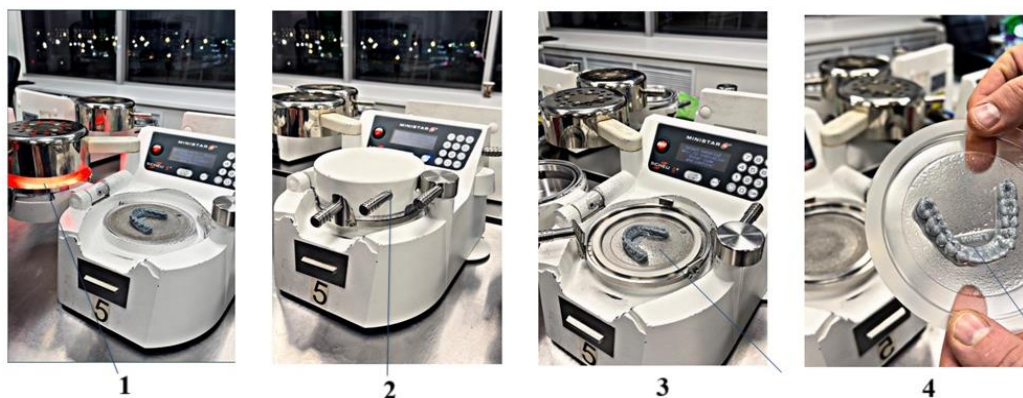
Термоформовочный агрегат фирмы Shueu-Dental, модель Ministar-S для изготовления элайнеров. 1 – ИК излучатель, 2 – герметичная пневмокамера, 3 – 3D копия челюсти, 4 – отформованная заготовка элайнера
